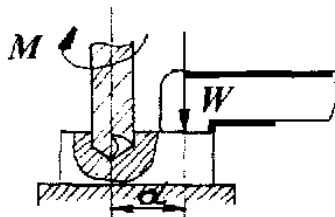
Затиск заготовки прихватами при свердлінні
